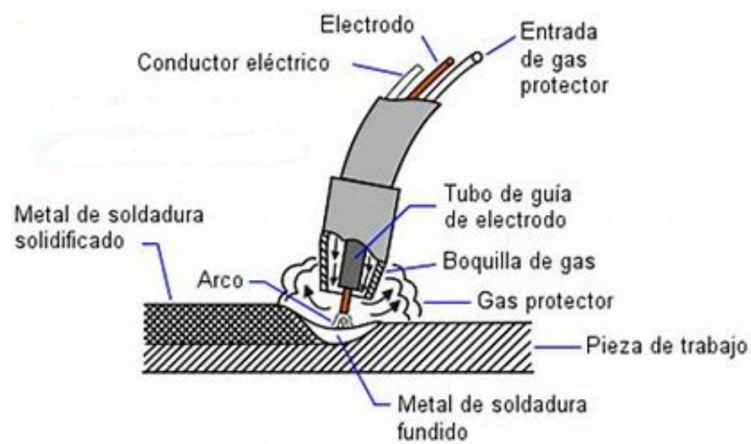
Soldadura GMAW (electrodo consumible)
